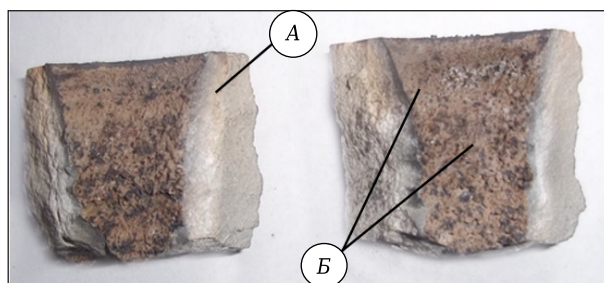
Фрагменты калибровочной вставки стакана-дозатора с отложениями неметаллических включений: А — тело калибровочной вставки; Б — отложения неметаллических включений
